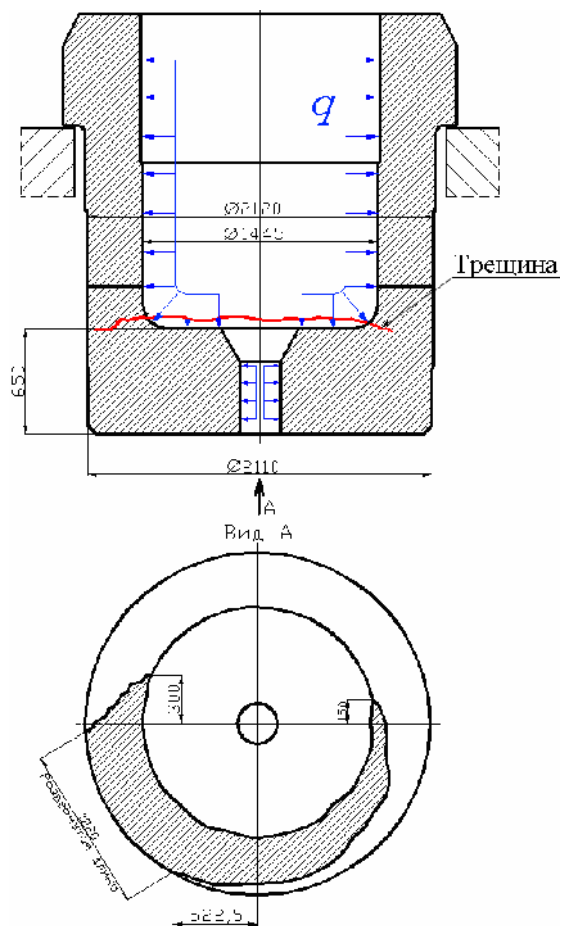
Схема нагружения цилиндра пресса силой 50 МН, расположение и размер трещины в днище цилиндра
